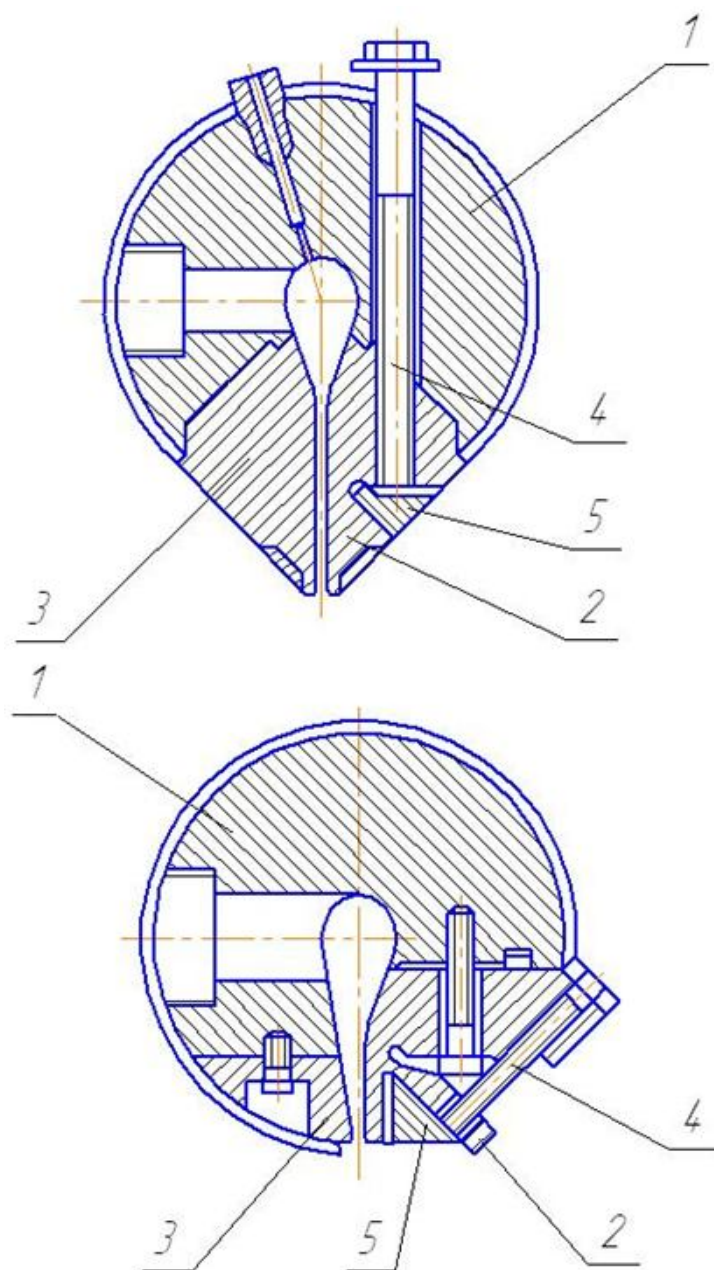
Переріз головок з пристроями для регулювання висоти щілини: 1 – корпус головки; 2 – пружно-деформована губка; 3 – нерухома губка; 4 – гвинт регулювання висоти щілини; 5 – проміжний клин.
